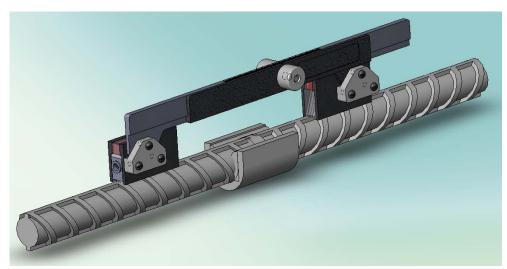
Комбинированный ультразвуковой преобразователь для контроля сварных швов арматуры $\Pi A123-1,8-65^0$. Внешний вид.
